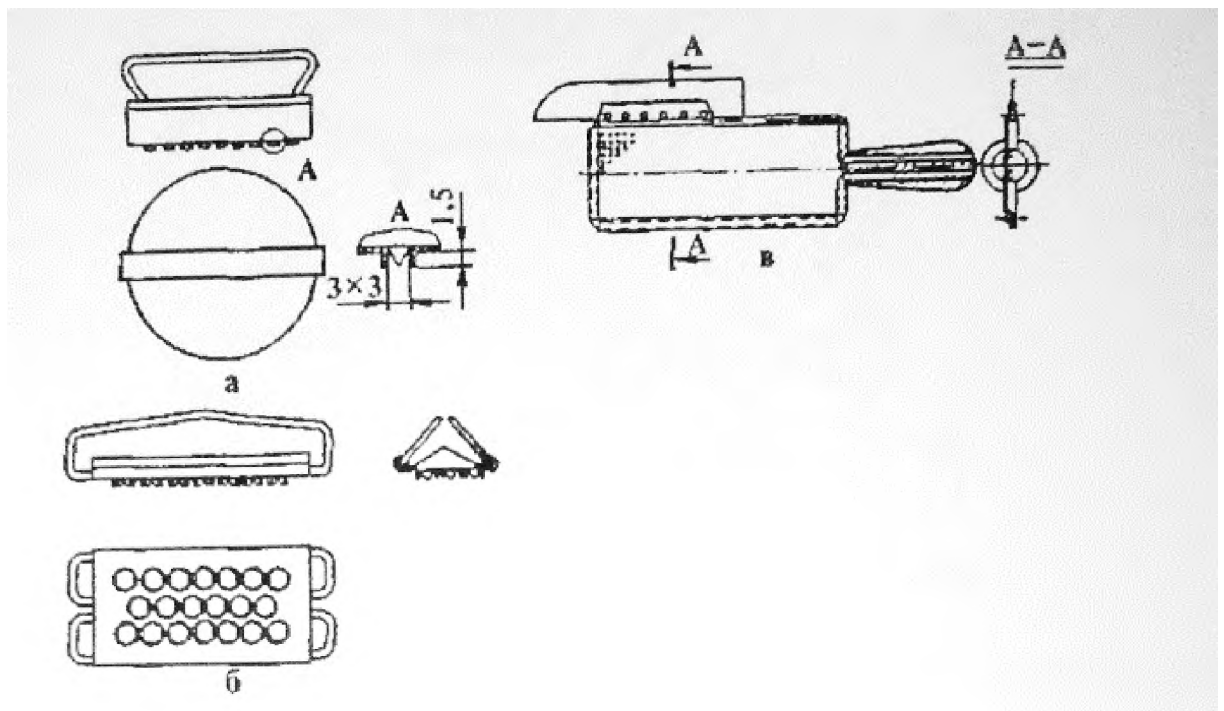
Інструменти з абразивною поверхнею для зняття луски:
